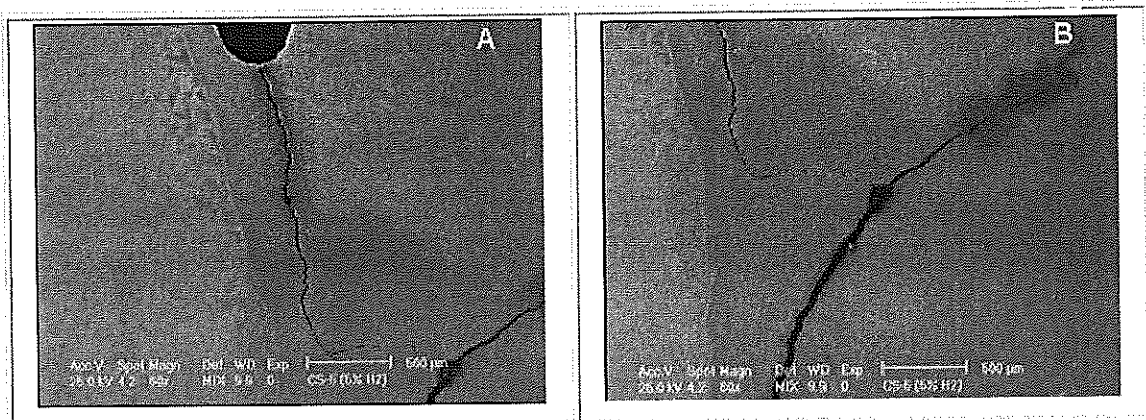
Muestra el inicio de la fisura por fatiga en la probeta 5. Se observa que comienza en el metal de soldadura y no sigue un patrón pues como podemos ver en B) desvia su dirección. Ataque: Villella.
